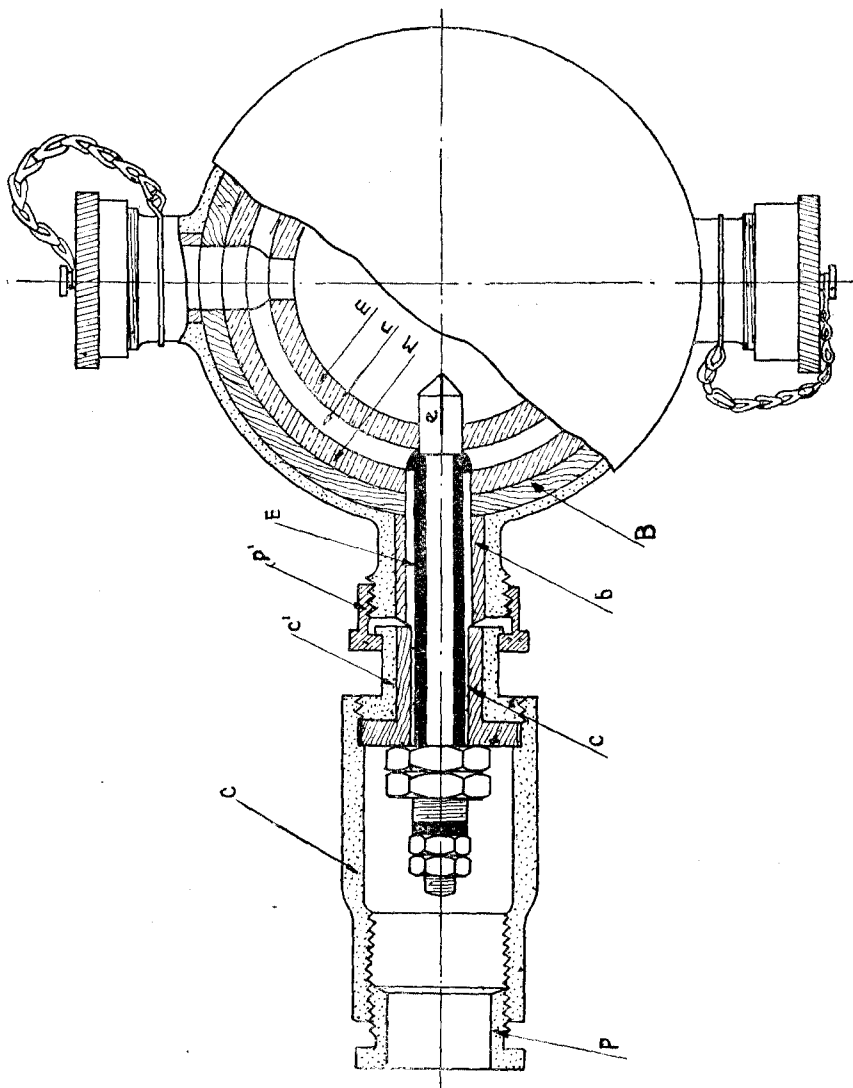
Caja metálica de empalme de tres direcciones. Planta y corte horizontal.
